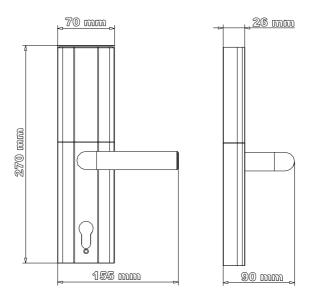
Dimensiones del alzado y perfil de la parte trasera de la cerradura.
